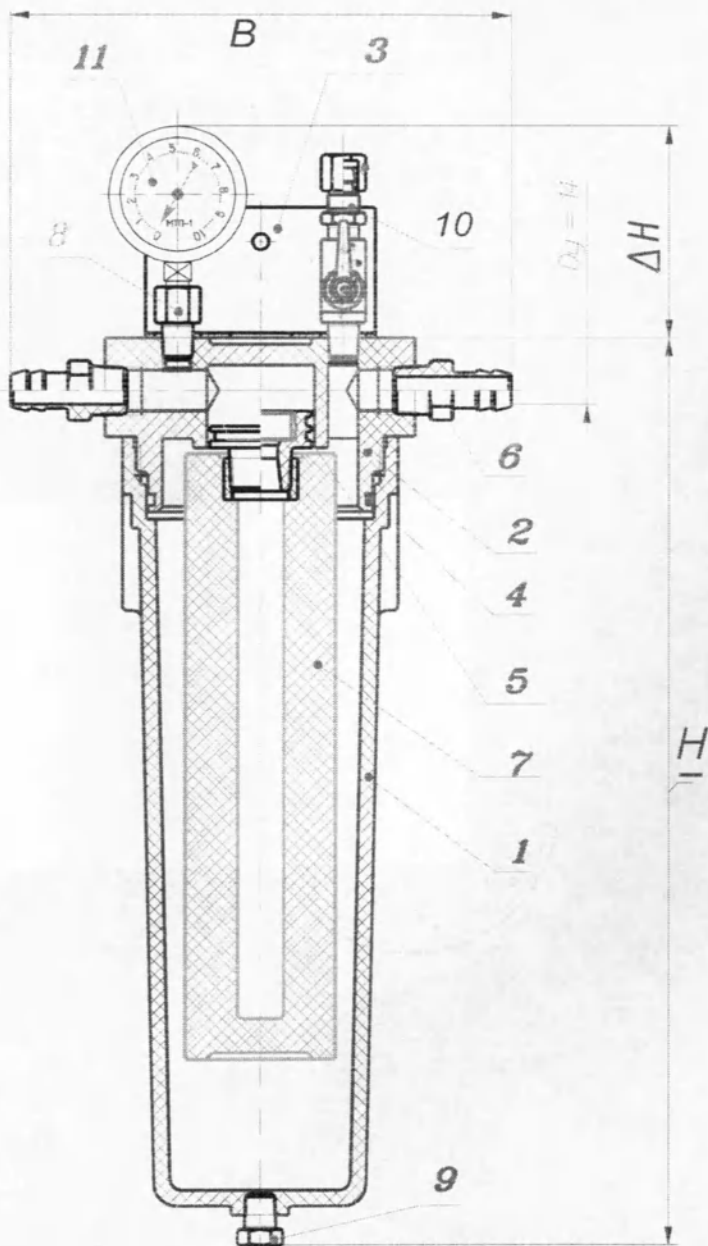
Одноразовый фильтродержатель ДФП-301L-250-A0 1 - колпак; 2 - корпус; 3 - кронштейн; 4 - посадочное место; 5 - адаптер; 6 - штуцер; 7 - фильтро-элемент; 8 - переходник; 9 - заглушка; 10 - кран; 11 - манометр.
